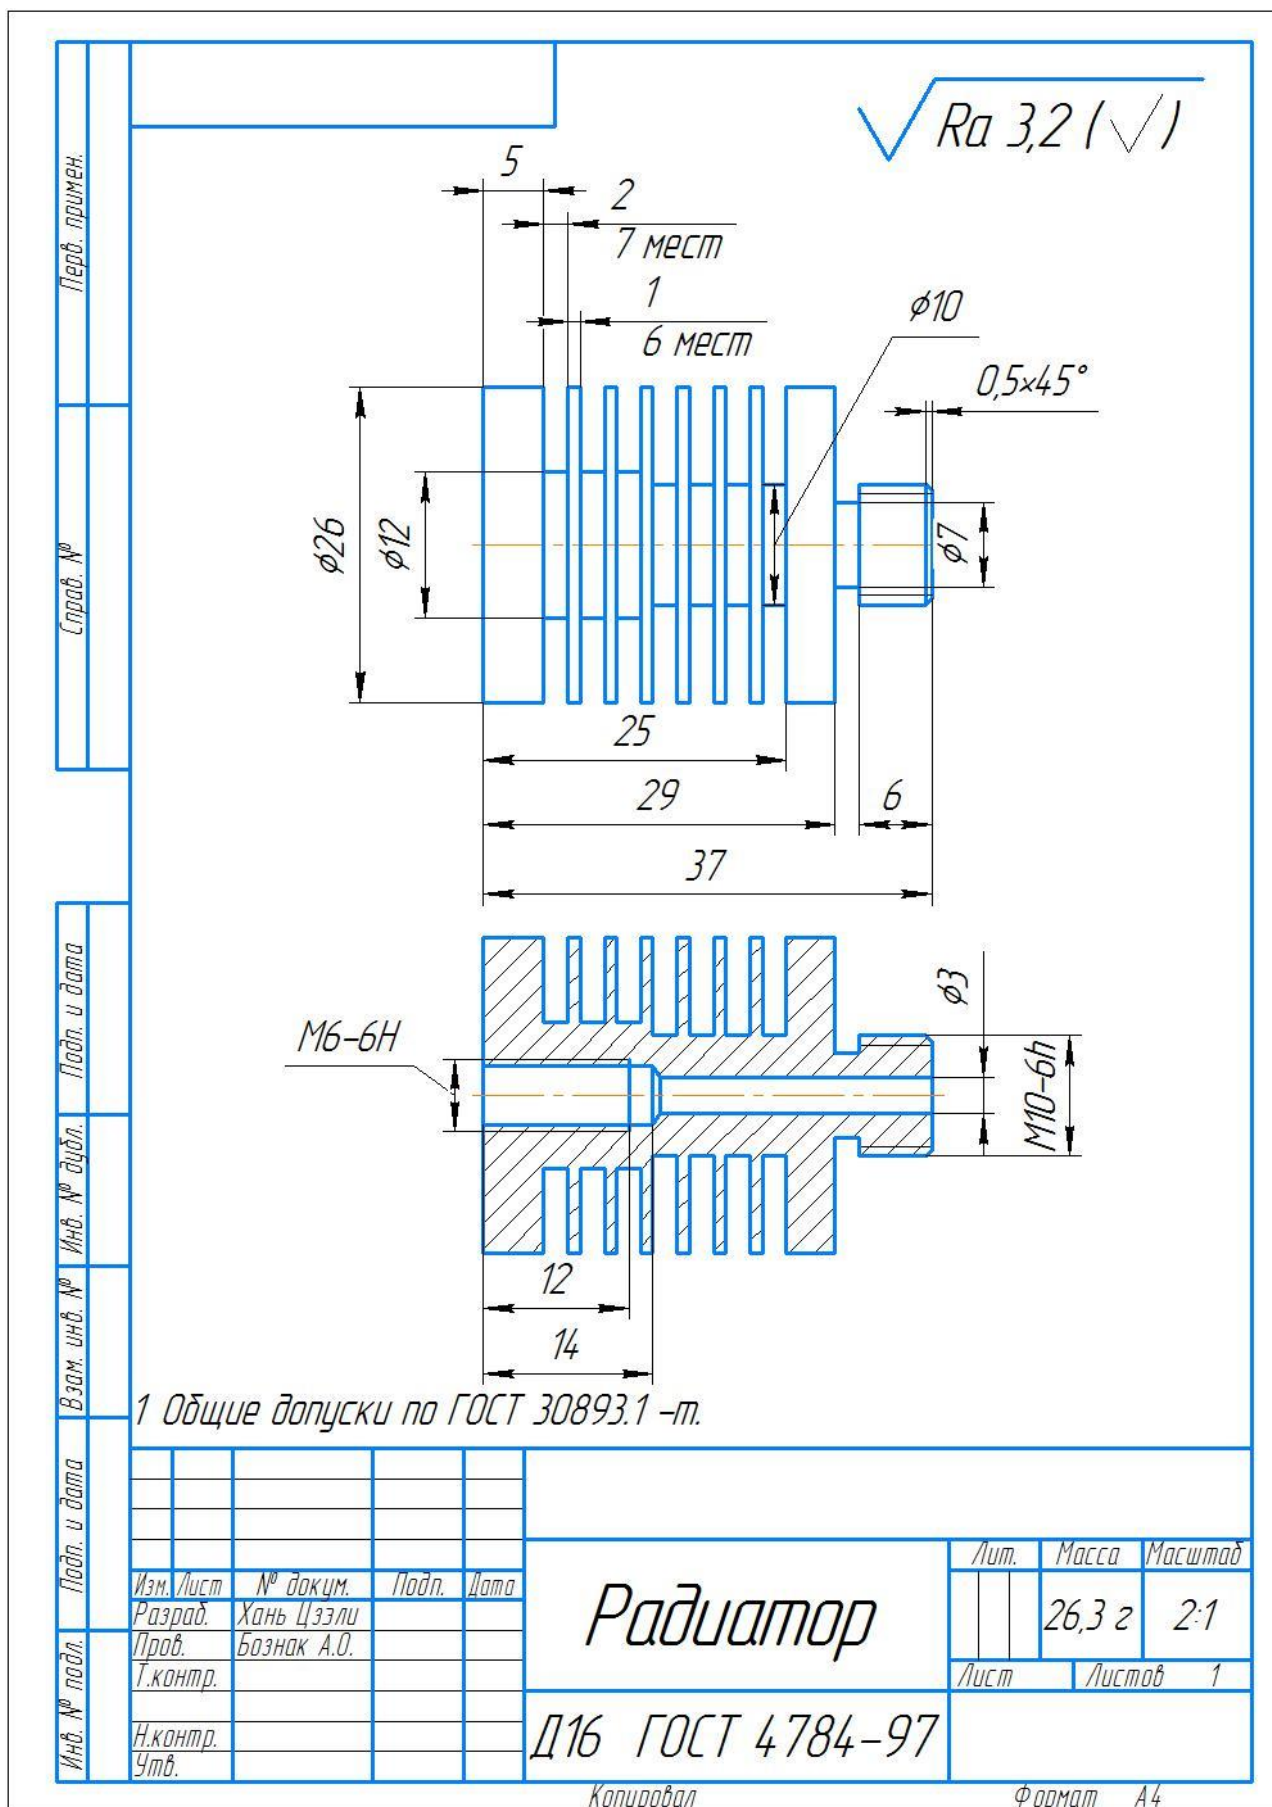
Чертеж детали «Радиатор»
